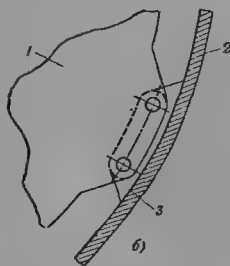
Установка промежуточных перегородок и их крепление к корпусу конденсатора.
